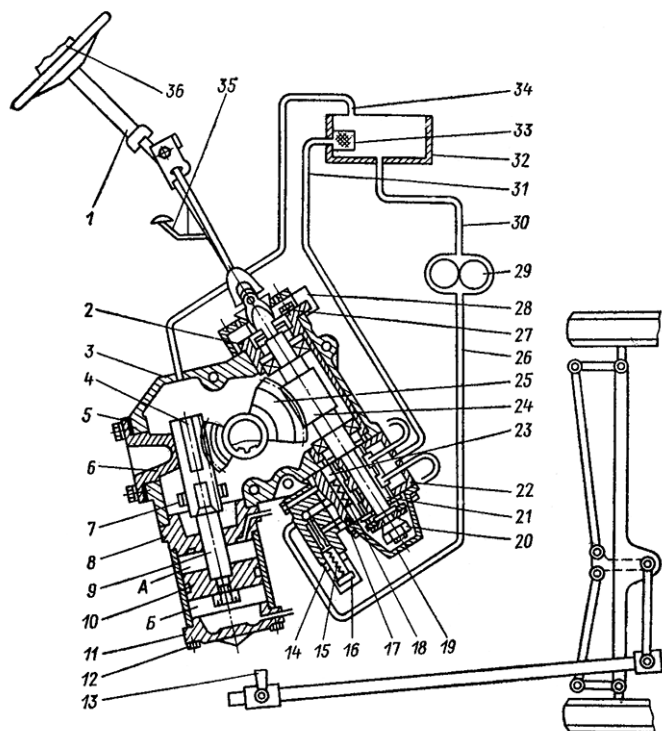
Схема рулевого управления трактора ЮМЗ-6КЛ с гидроусилителем: 1 — рулевая колонка; 2 — эксцентричная втулка; 3 — корпус; 4 — рейка; 5 — регулировочные прокладки; 6 — упор; 7 — палец; 8 — верхняя крышка цилиндра; 9 — шток; 10 — поршень; 11 — нижняя крышка цилиндра; 12, 27 — болты; 13 — сошка; 14 — контргайка; 15, 18 — пружины; 16 — винт; 17 — предохранительный клапан; 19, 28 — крышки; 20 — сферическая гайка; 21 — шайба; 22 — корпус распределителя; 23 — плунжер; 24 — червяк; 25 — сектор; 26 — нагнетательный маслопровод; 29 — масляный насос; 30 — всасывающий маслопровод; 31 — сливной маслопровод; 32 — масляный бак; 33 — фильтр; 34 — дренажный маслопровод; 35 — педаль; 36 — зажим
